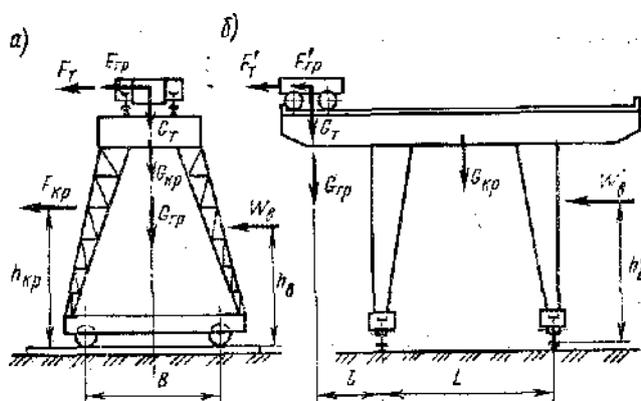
Схема к определению грузовой устойчивости козловых кранов вдоль (а) и поперек [б) подкранового пути
